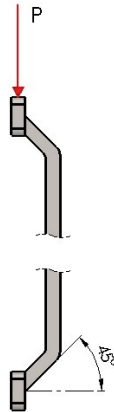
Carga aplicada sobre la viga central (Fuente: propia)
